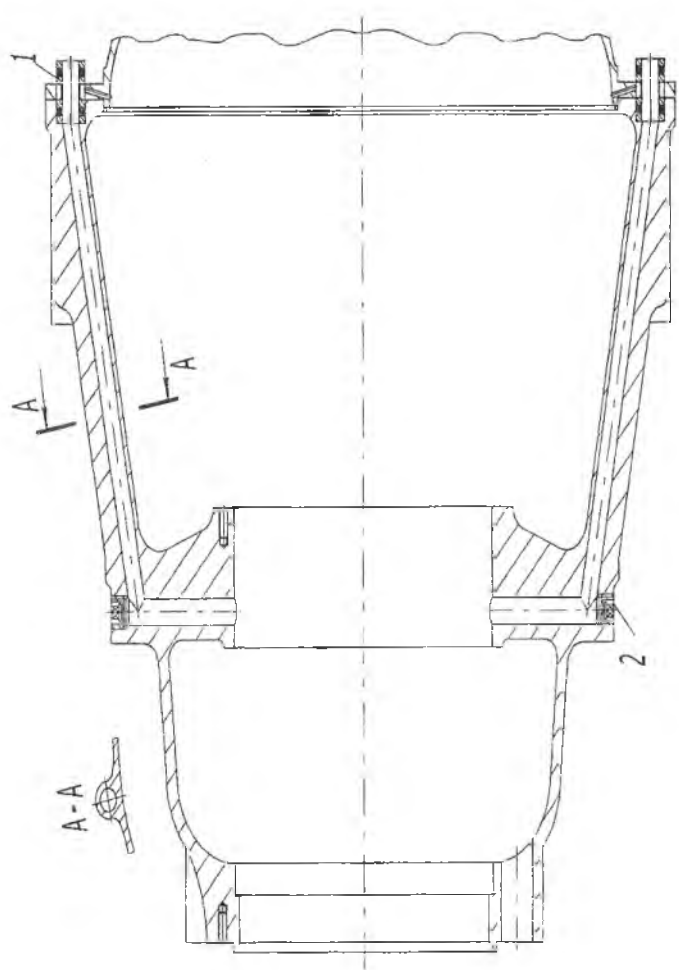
Масляные каналы в корпусе редуктора ТВД АИ-20
